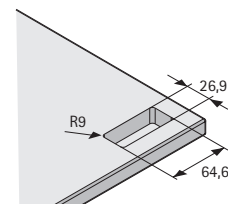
Fräsbild zum Einbau des Handschalters LegaDrive Touch Inlay Basic mit Gummilamellen
